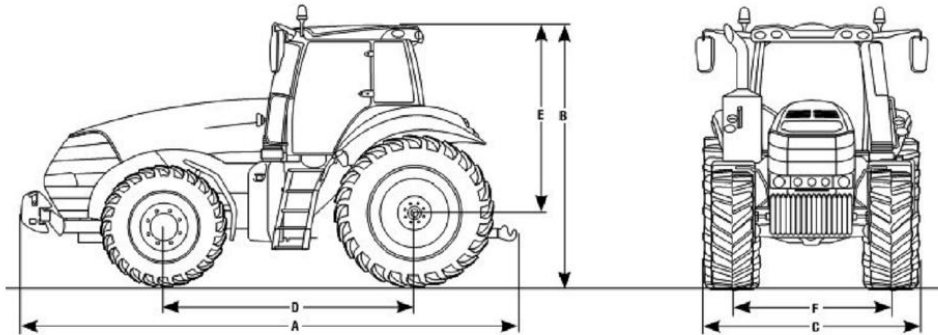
Dimensioni di trattore gommato di grandi dimensioni.
